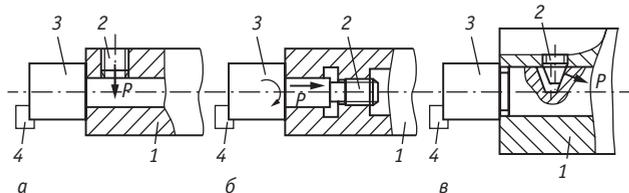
Типы цилиндрических соединений модулей: а – с односторонним прижимом винтом; б – с осевой затяжкой; в – со смещенным крепежным винтом сбоку (1 – резцовая головка, 2 – крепежный винт, 3 – сменная наладка или державка, 4 – резцовая головка). Направление зажимной силы P показано стрелкой
